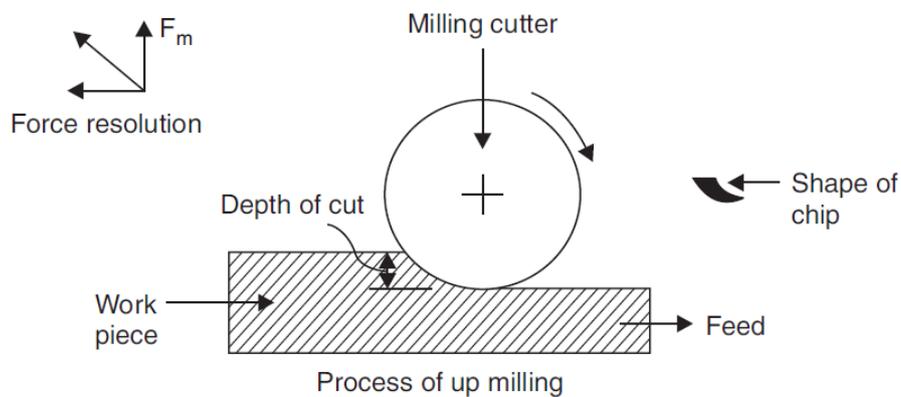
Esquema del proceso de fresado. H. N. Gupta, Manufacturing Processes, 2009.
